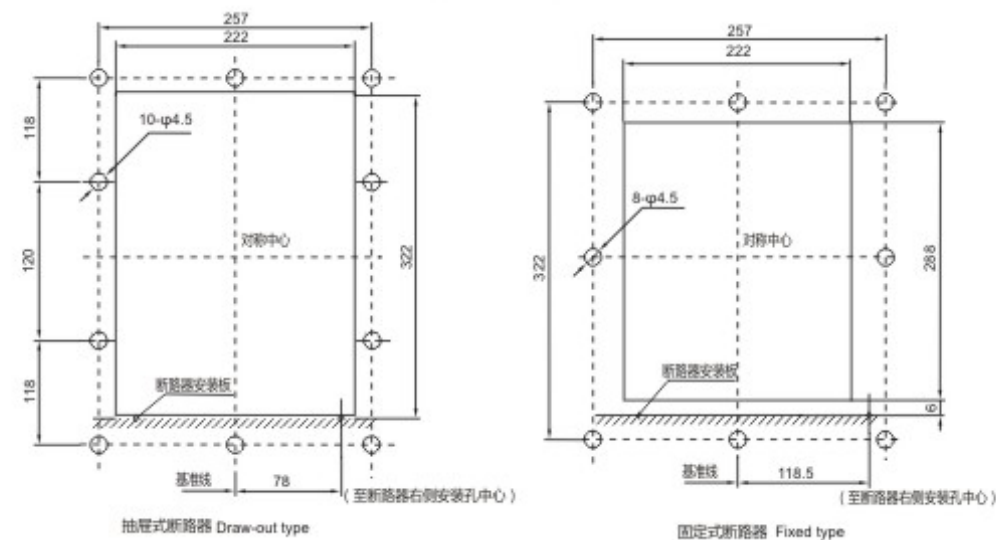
FSW2-1600/3P, 4P断路器门框开孔与安装尺寸
